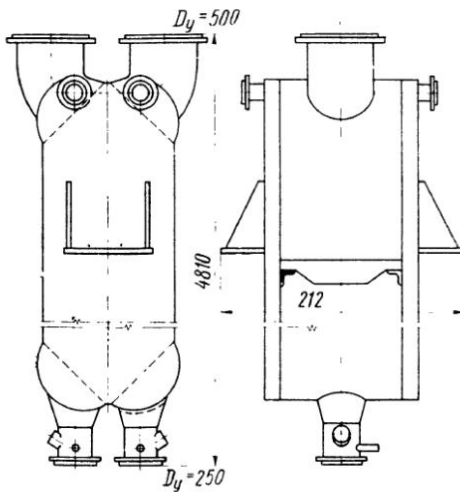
Сварная неразборная пластинчатая греющая камера для выпарного аппарата
